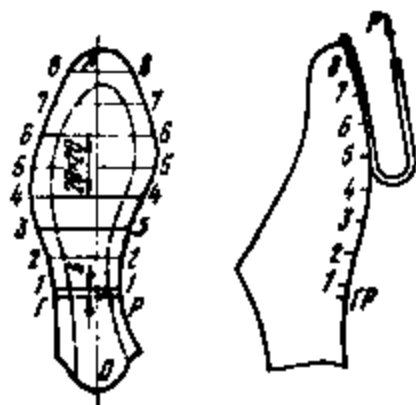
Схема разметки и отрыва подошвы от обуви химическими методами крепления
